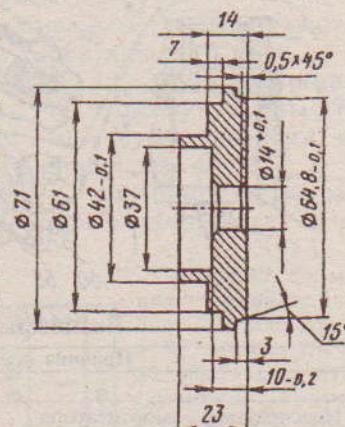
Оправка для запрессовки манжет и наружного подшипника ведомого вала
